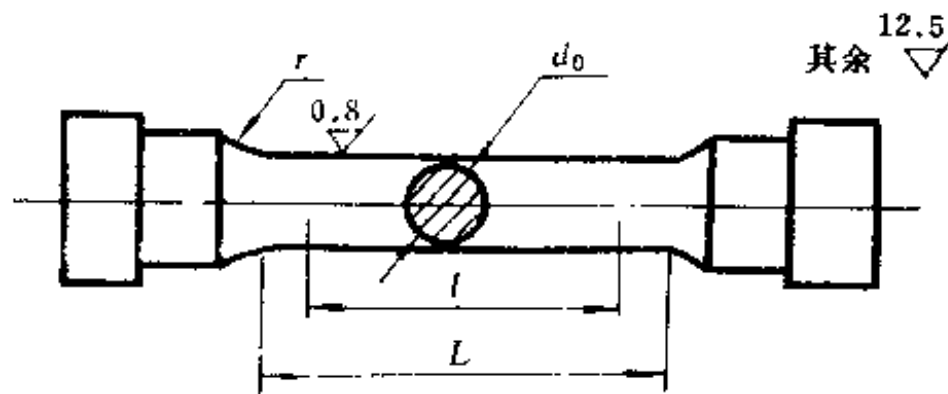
焊缝及熔敷金属拉伸试样(二)
